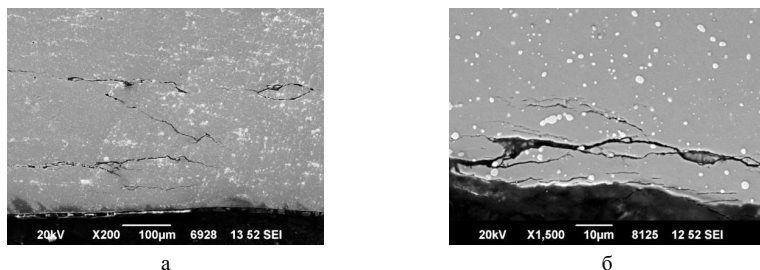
Строение вскрытой трещины на дорожке качения наружного кольца подшипника № 1:
